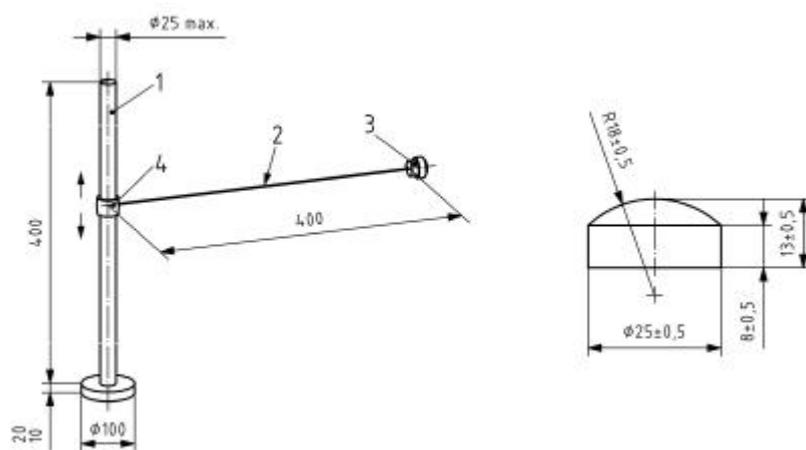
Prendas de ropa: barra 40 cm + cadena 40 cm + botón de trenca Ø25 mm (Fuente SFS-EN1176).
